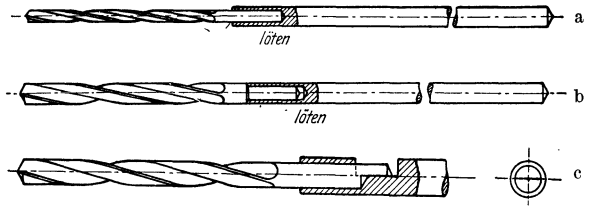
Verlängerung für Bohrer mit zylindrischem Schaft.
